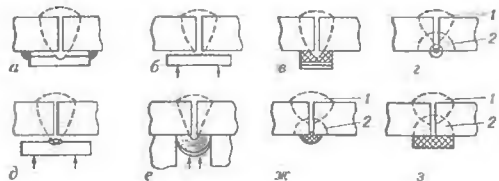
Схеми пристроїв для утримання зварювальної ванни та шляху й формування зворотного валика при зварюванні під флюсом.
